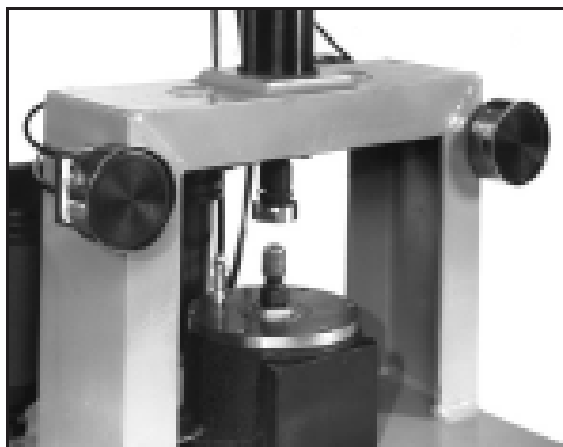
Fresagem Off-line (TECNOWELDING, 2004.)
